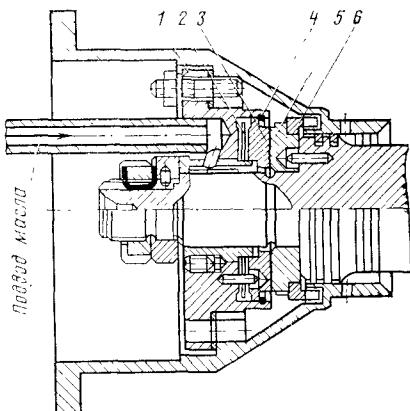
Опорно-упорный подшипник турбокомпрессора ТК-23:
